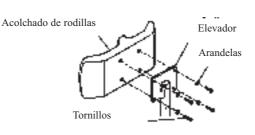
REEMPLAZAR EL ACOLCHADO DE LAS RODILLAS
